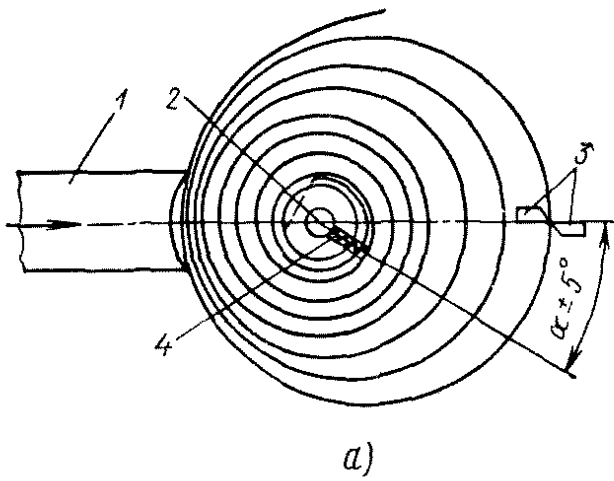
Приспособление для отрезки внешнего витка спирали:
